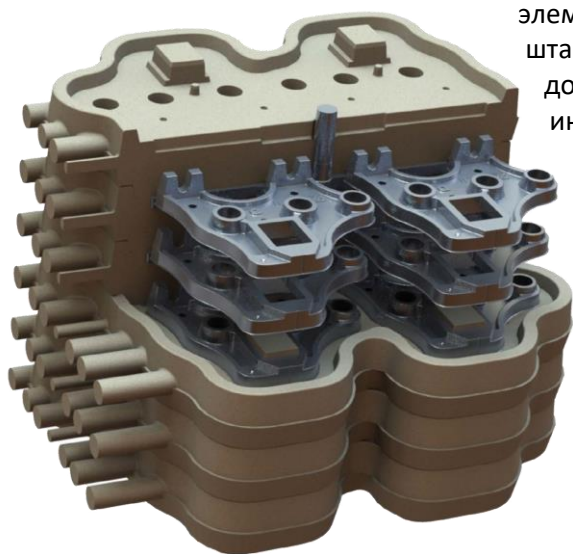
Расположение отливки из серого чугуна в форме с несколькими размещёнными друг над другом уровнями
